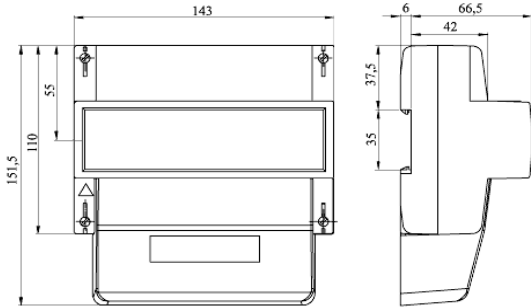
Загальний вигляд лічильника CE303-U в корпусі R33
